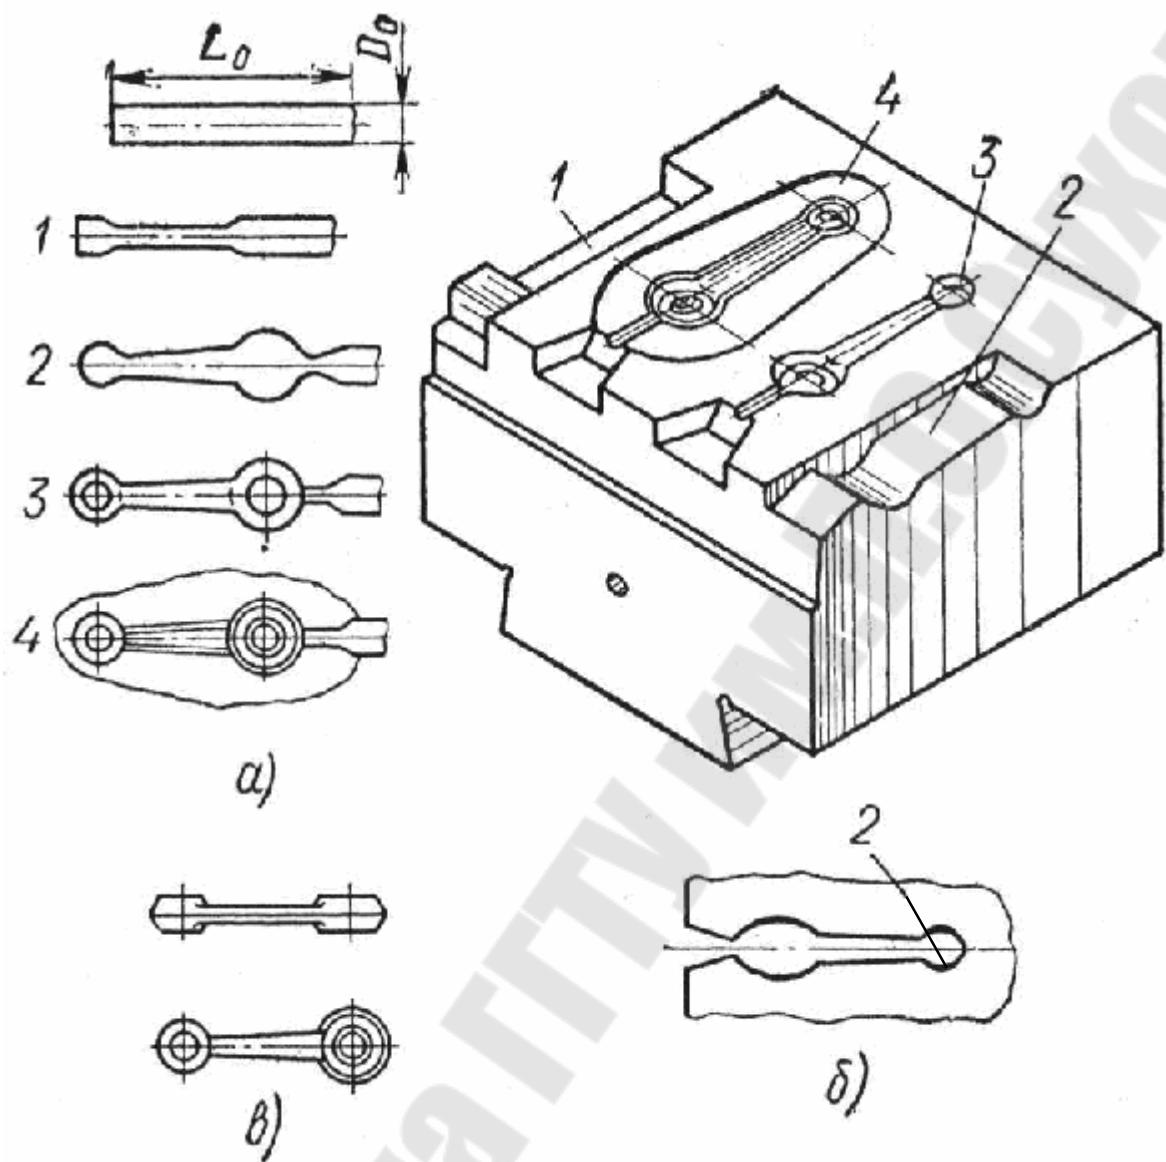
Многоручьевой штамп для открытой штамповки поковки для шатуна:
